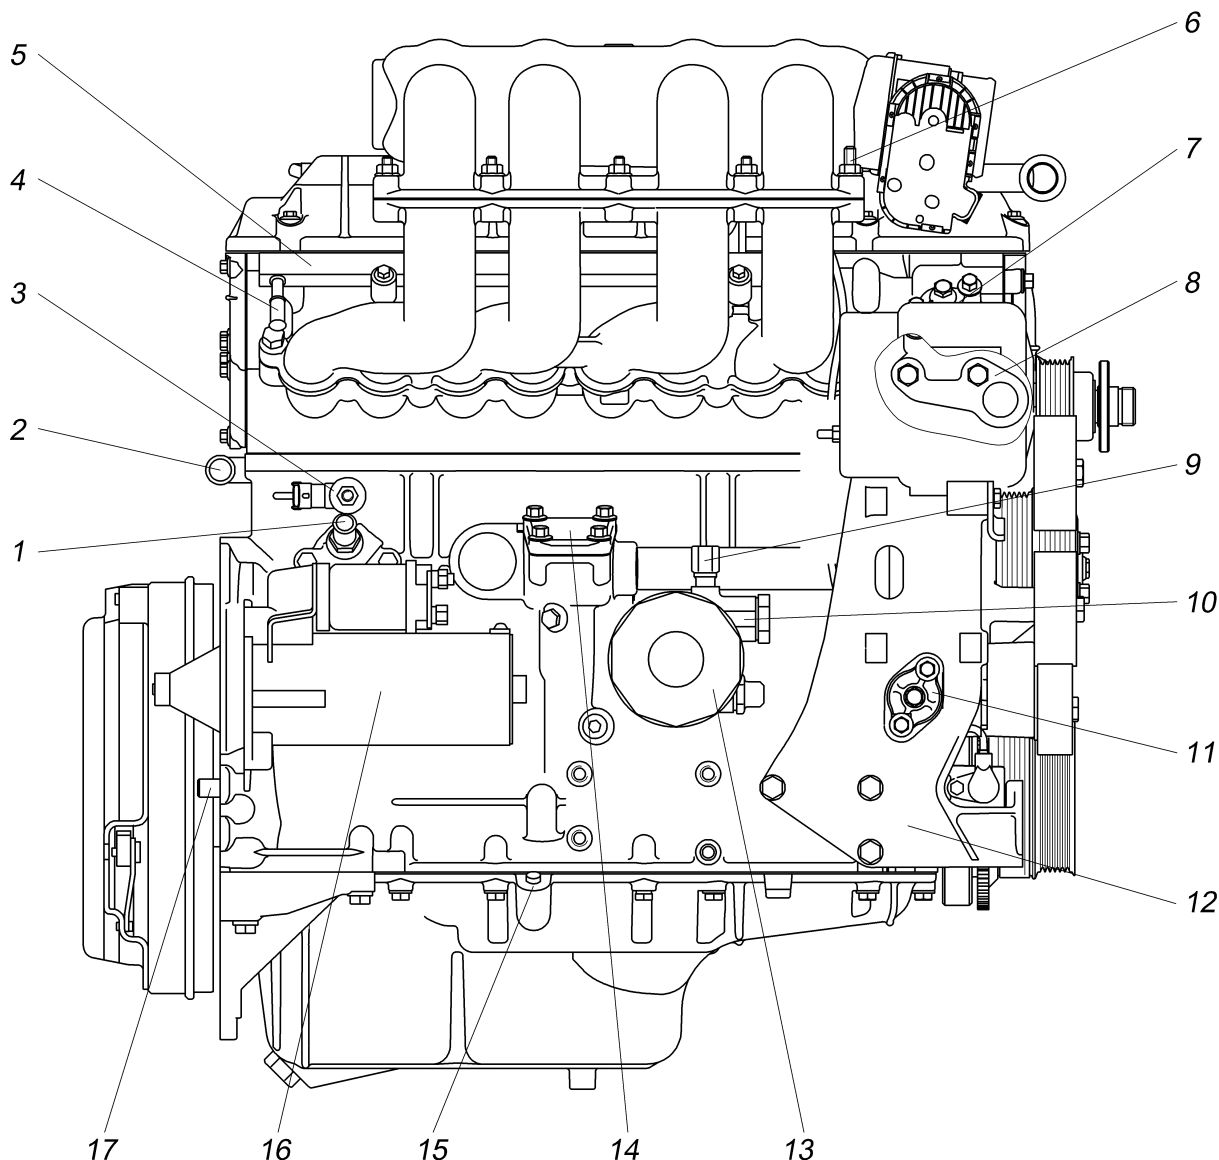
Вид слева двигателя ЗМЗ-40904.10
